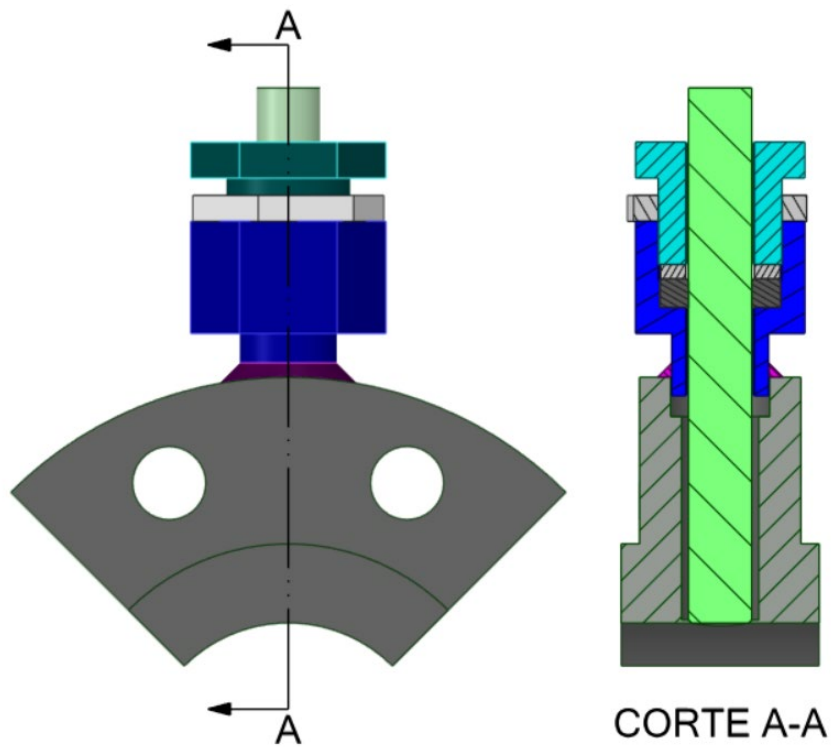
Dispositivo con sello elastomérico de sección rectangular, pero sin sujeción mecánica, nótese el diseño de la soldadura tipo socket o por encaje.
